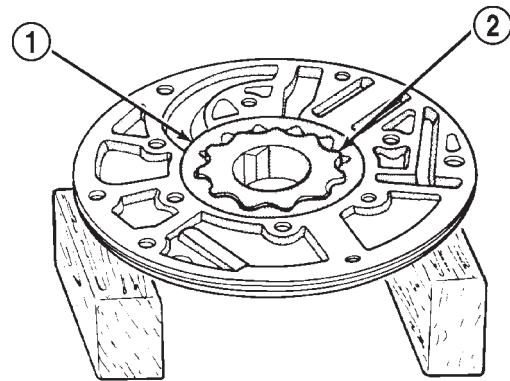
Apoyo de la bomba e instalación del engranaje externo
